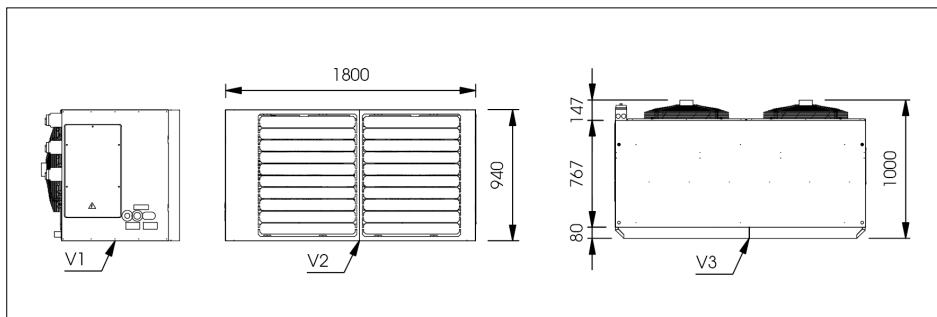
Onderdelen voor installatie van de MISTRAL MDX 60. (V1: Achteraanzicht, V2: Zij aanzicht links)
